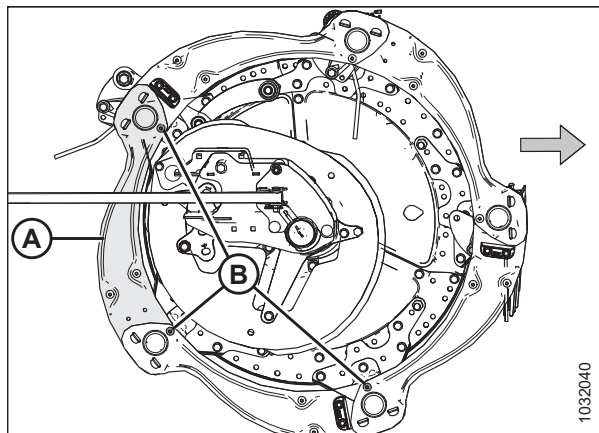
Бокові щитки мотовила — зовнішній кінець ексцентрика
